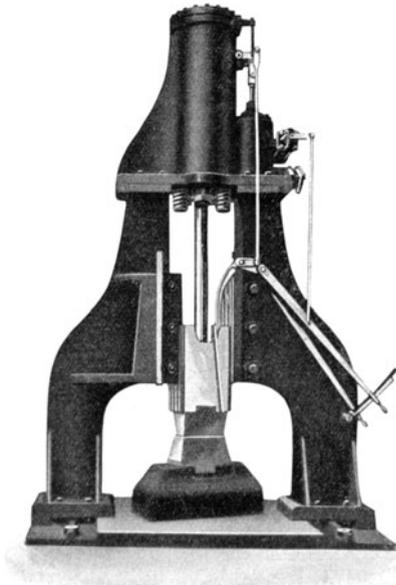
Hand- und Selbststeuerung der Buffalo Foundry & Machine Co. in Buffalo.
